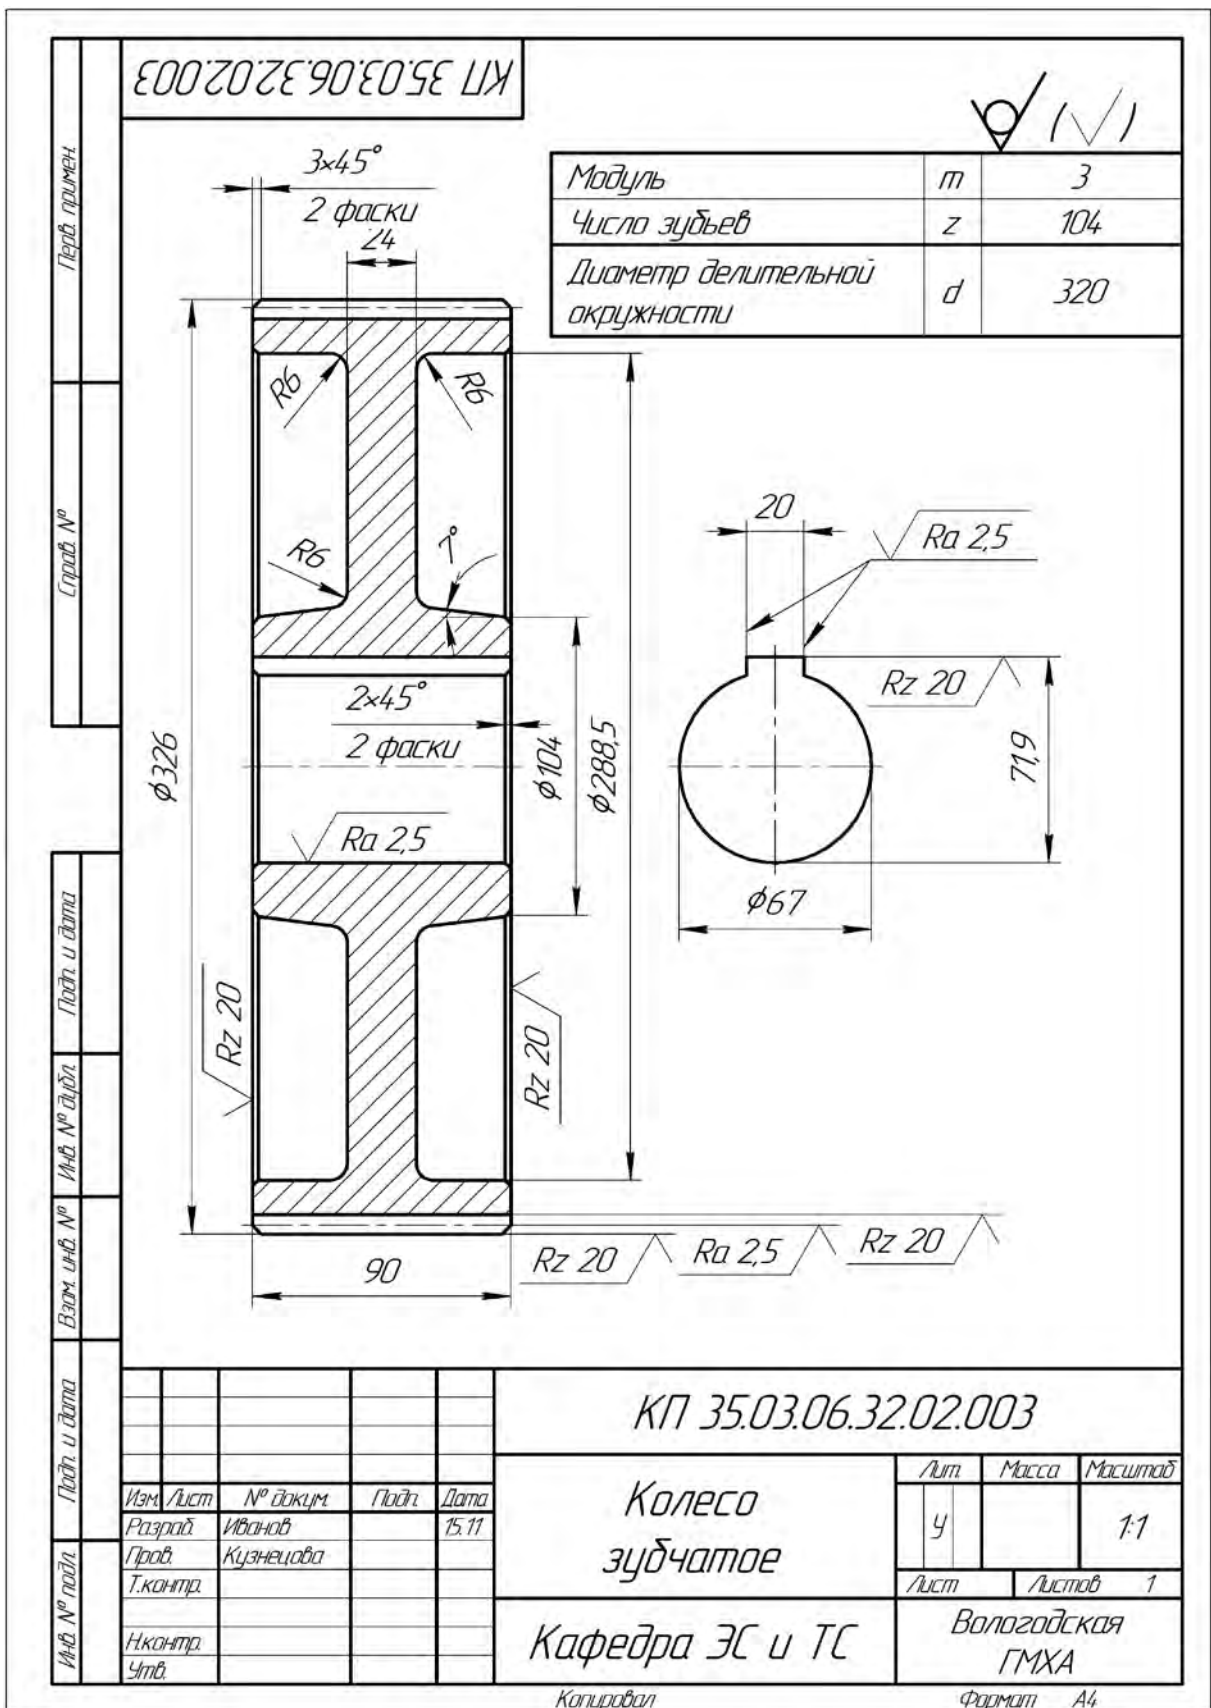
Пример выполнения рабочего чертежа зубчатого колеса
